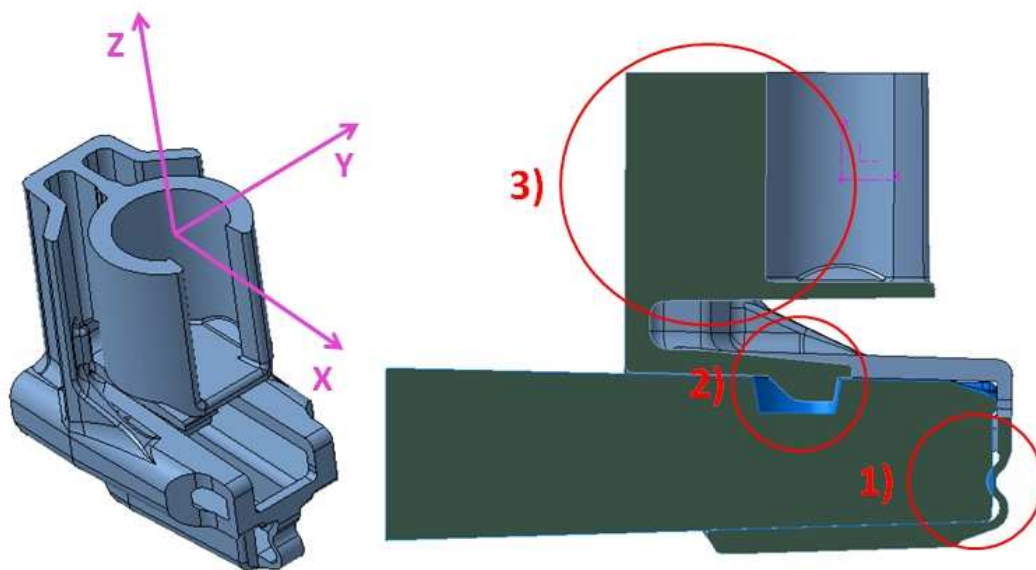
Konstrukční návrh – varianta 2: návrh přídržovacích žebër.
